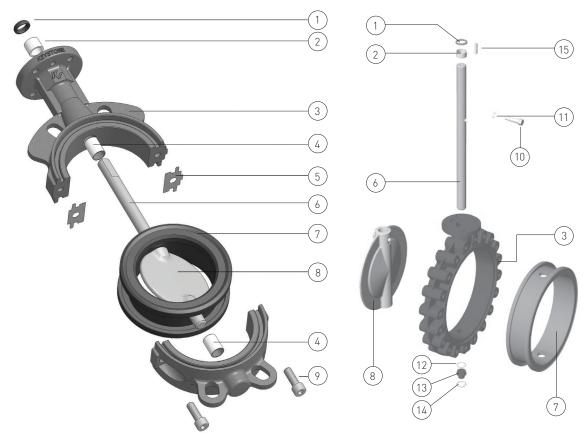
/16 разнесенный вид (корпуса из ковкого чугуна)
